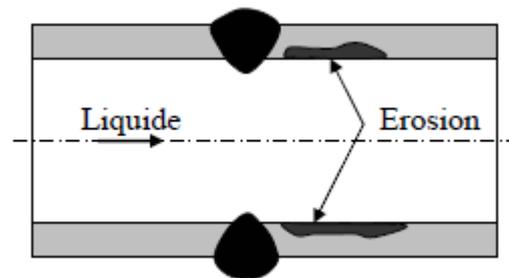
érosion - corrosion due à des turbulences produites par les cordons de soudure
